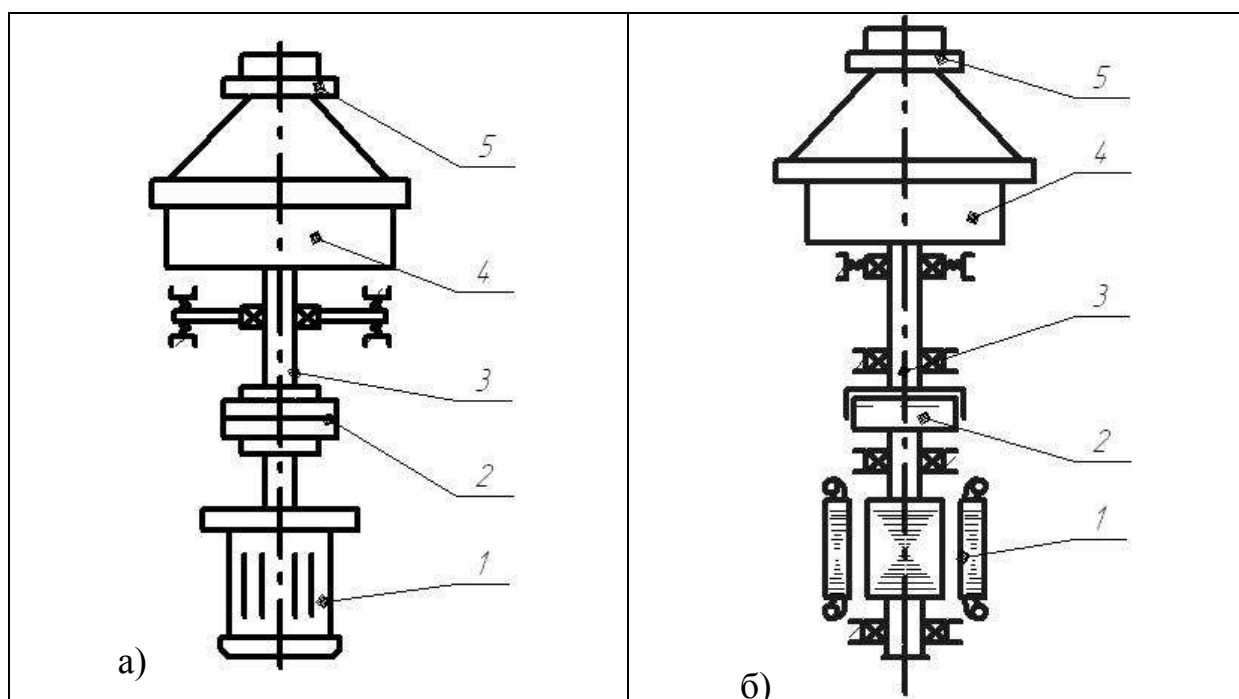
Кинематические схемы безредукторных сепараторов молока:
